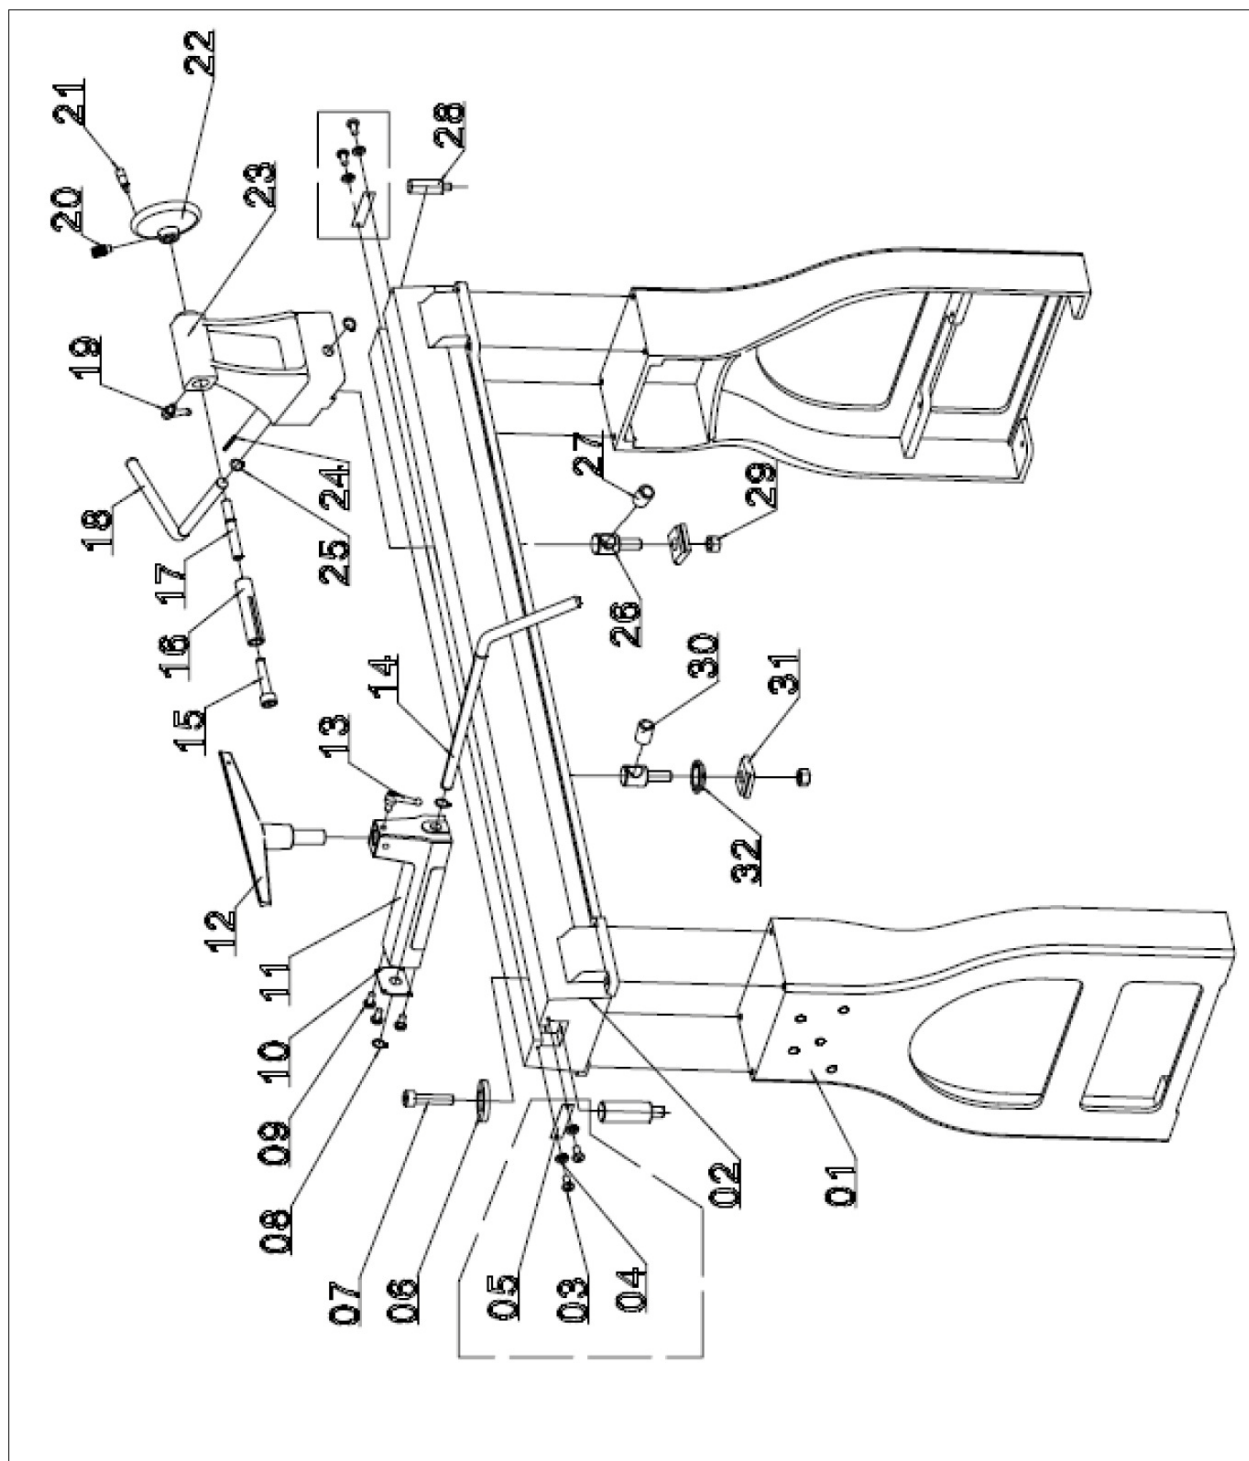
Схематический чертеж 1 Токарный станок по дереву DB 1202
